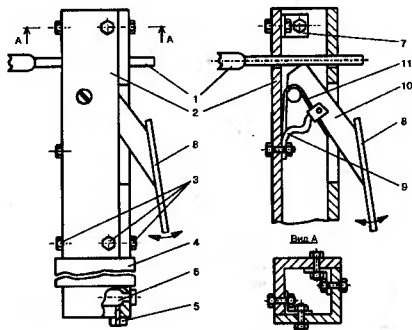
Чертеж корпуса держателя электродов из трубы  $\varnothing 3/4"$
